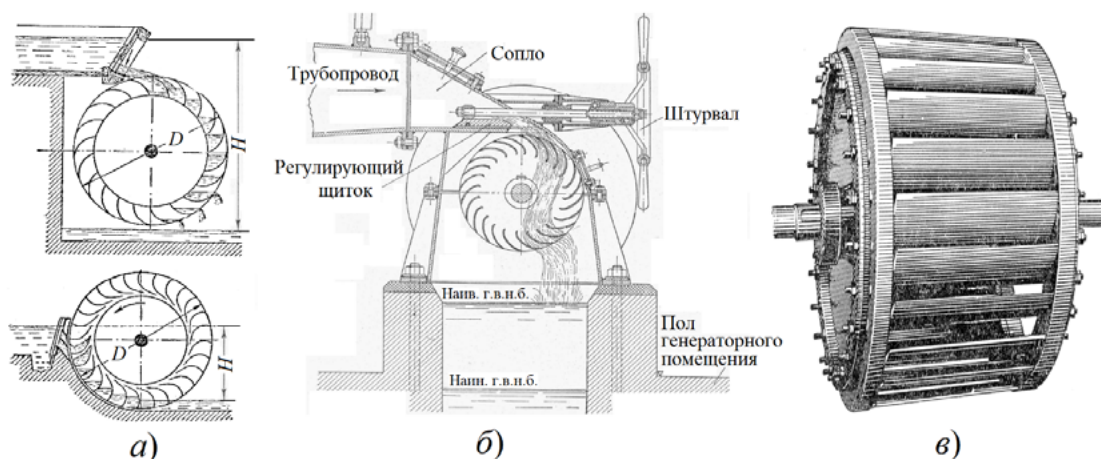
Гидравлический двигатель с верхненаливными колесами.
